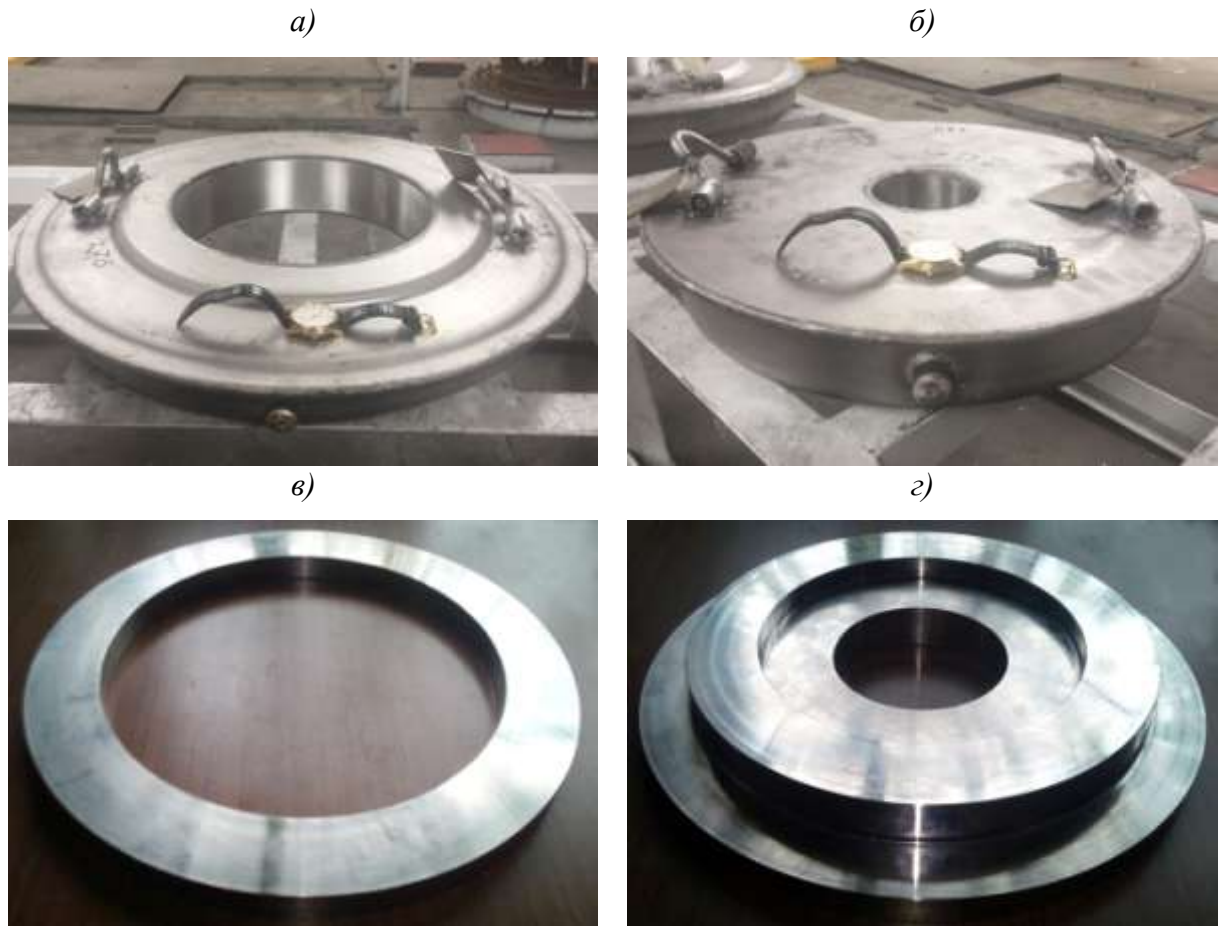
Полноразмерные заготовки дисков из высокожаропрочного никелевого сплава марки ВЖ178П: а, б – перед ГИП; в, г – после механической обработки
